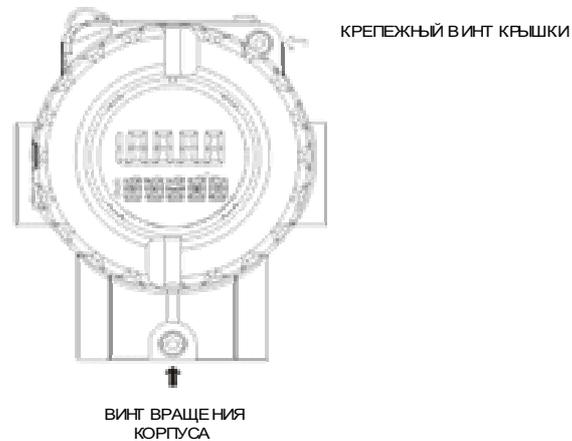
Крепежный винт и винт вращения корпуса
